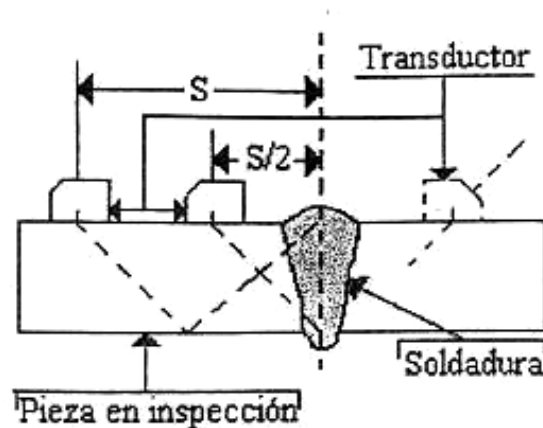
INSPECCIÓN CON PALPADOR DE HAZ ANGULAR
